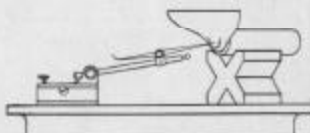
Centrage d'une Pièce de Forme Irrégulière
